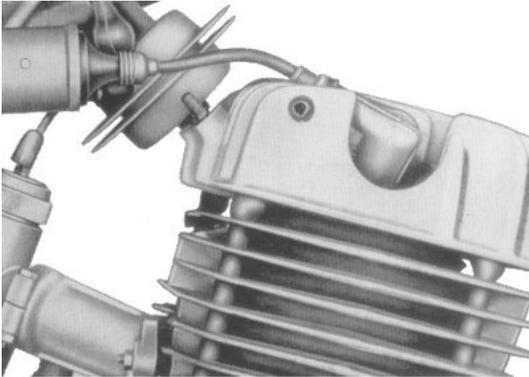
Stellung der Gummielemente der oberen Motoraufhängung beim Auswechseln
